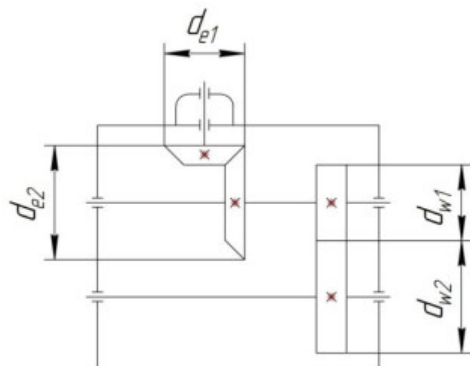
Кинематическая схема коническо-цилиндрического редуктора
